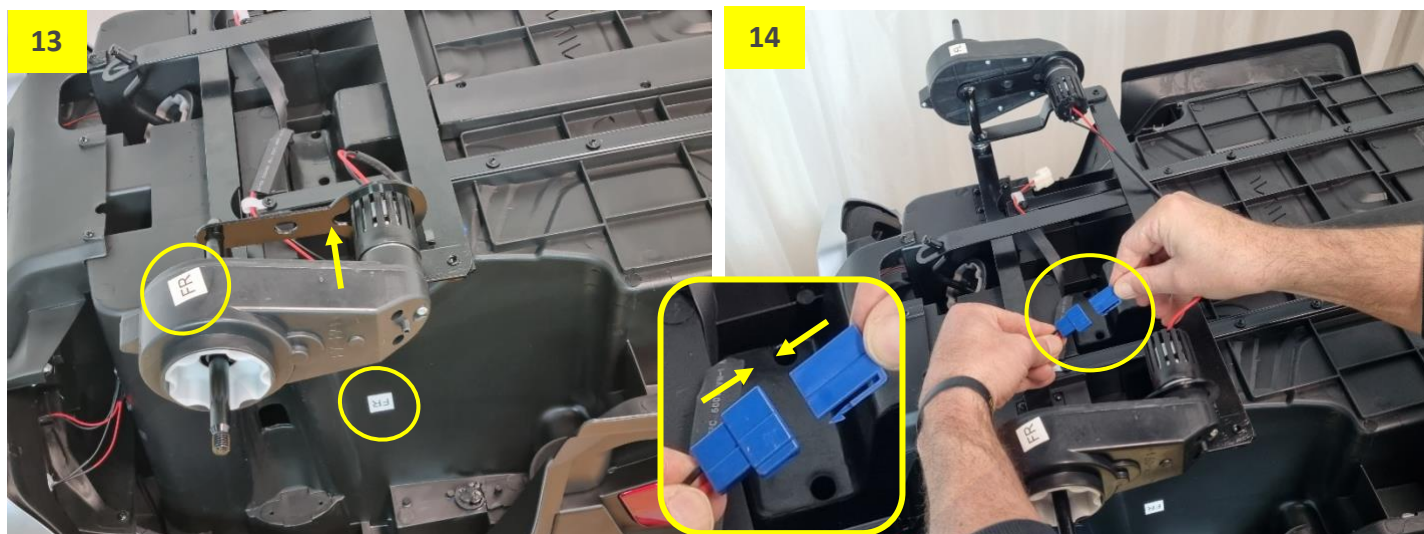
a 6: Nápravu přišroubujte (4+4 šroubky). Připravte si přední a zadní motory (FR=přední pravý / FL=přední levý / R=zadní pravý / L=zadní levý).
